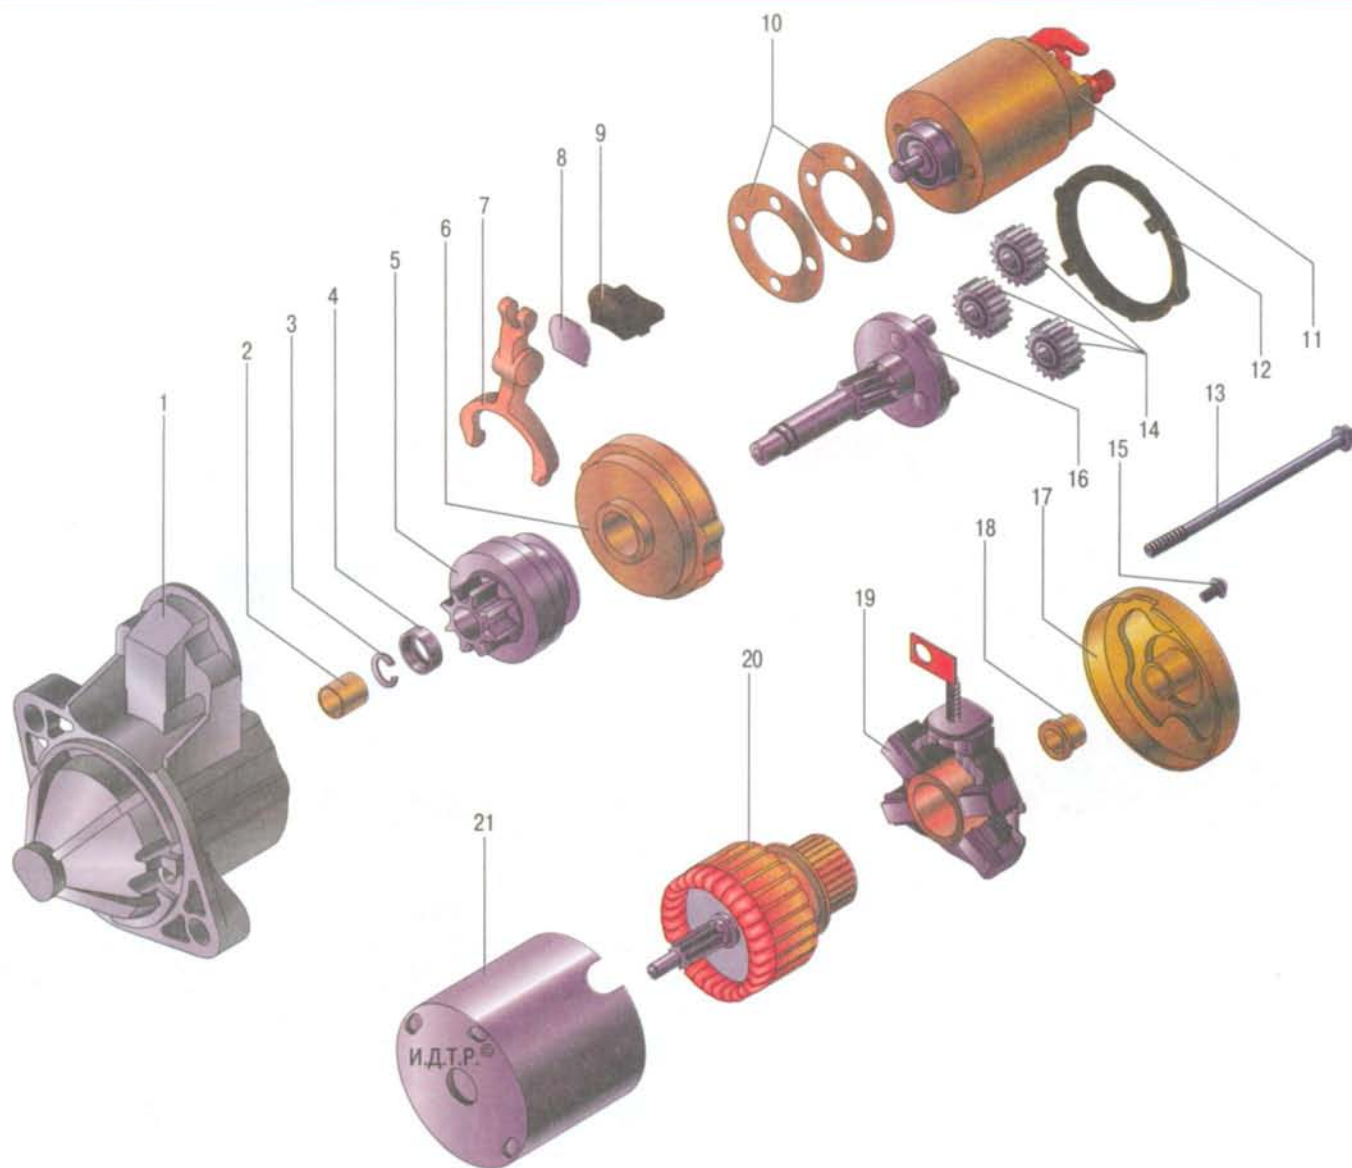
Детали стартера: 1 – крышка со стороны привода; 2, 18 – втулки подшипников; 3 – стопорное кольцо муфты привода; 4 – упорное кольцо муфты привода; 5 – муфта привода; 6 – коронная шестерня планетарного редуктора; 7 – рычаг привода; 8 – накладка опоры рычага привода; 9 – демпфер опоры рычага привода; 10 – регулировочные прокладки; 11 – тяговое реле; 12 – уплотнительное кольцо планетарного редуктора; 13 – планетарная шестерня; 14 – вал привода; 15 – стяжной болт; 16 – винт крепления крышки со стороны коллектора к статору; 17 – крышка со стороны коллектора; 18 – щеткодержатель; 19 – ротор; 20 – статор
